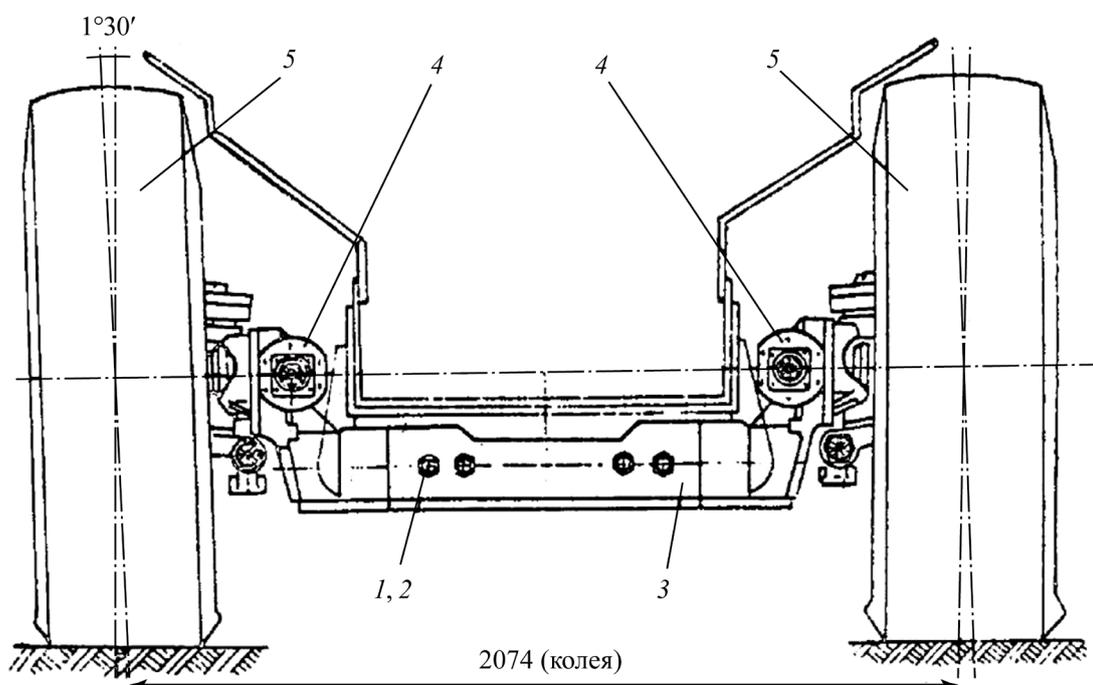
Задний мост самоходного вагона: 1, 2 – болт и гайка; 3 – стержень балки моста; 4 – корпус конического редуктора; 5 – колесо ходовое
